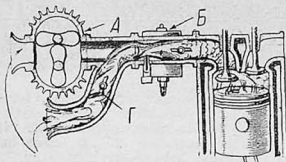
Схема расположения компрессора на автомобиле Мерседес-Бенц.
